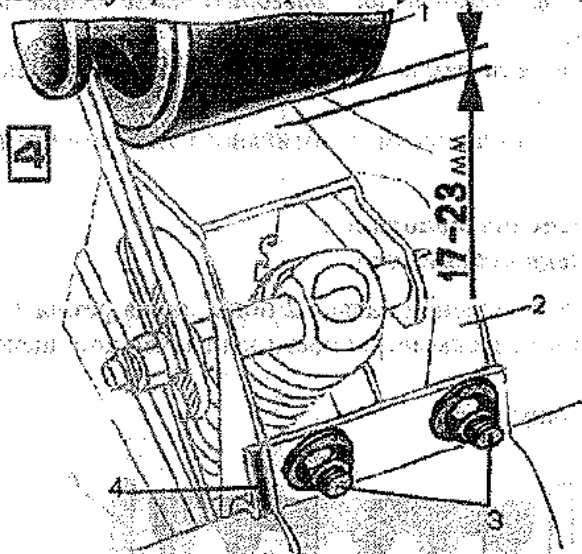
Схема регулировки зазора между боковиной кронштейна и шкивом двигателя: 1-шкив двигателя; 2-опорный кронштейн; 3-болты; 4-регулирующие прокладки
